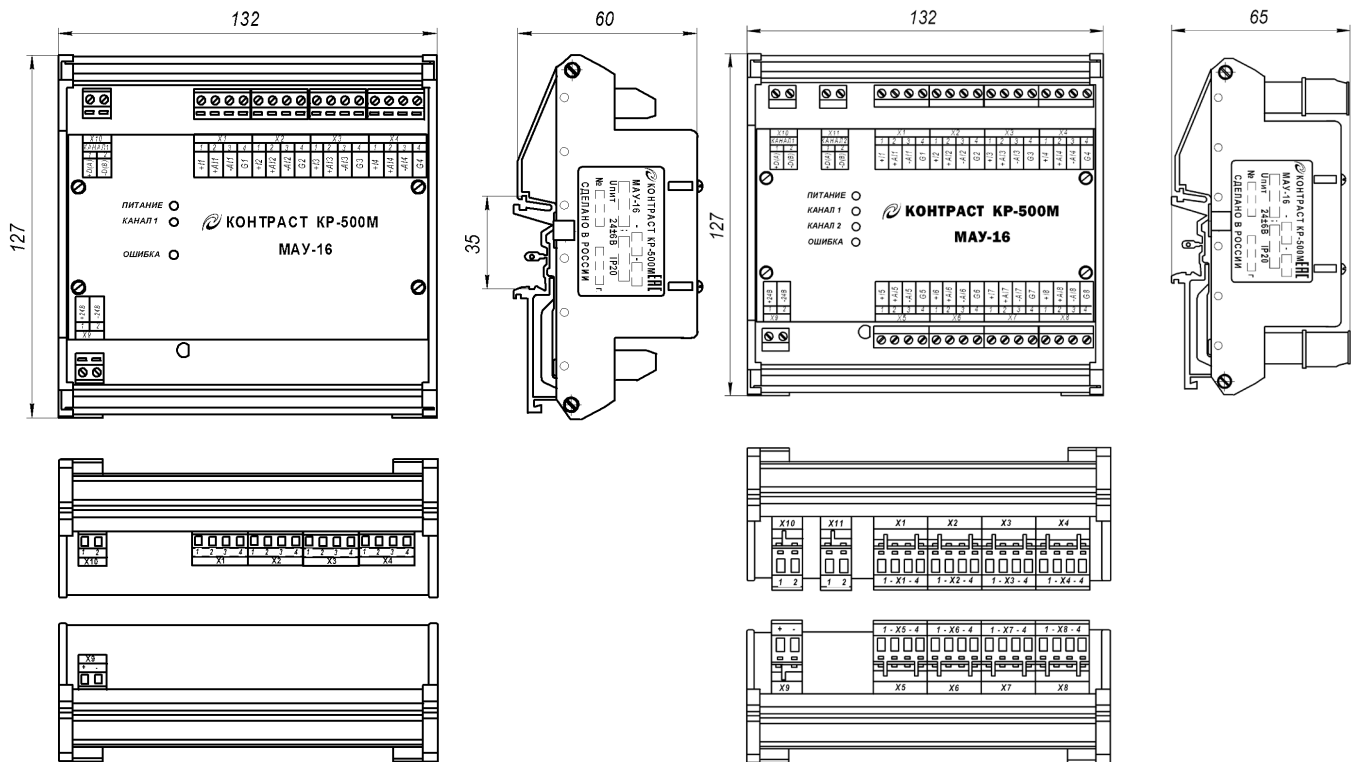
а) - габаритно-установочные размеры модуля МАУ-16-00,-01
